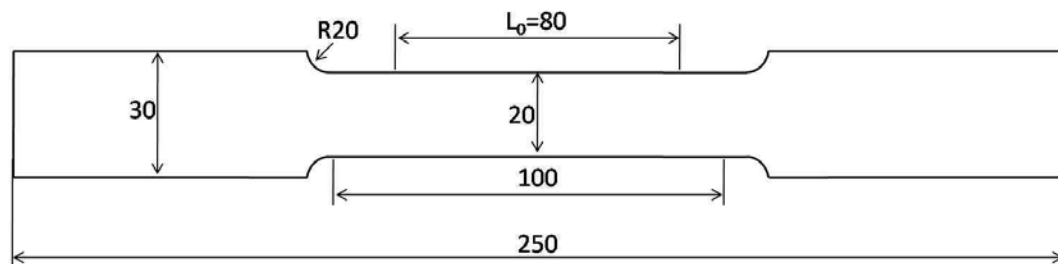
Dimension en mm de l'éprouvette de traction uni-axiale.
